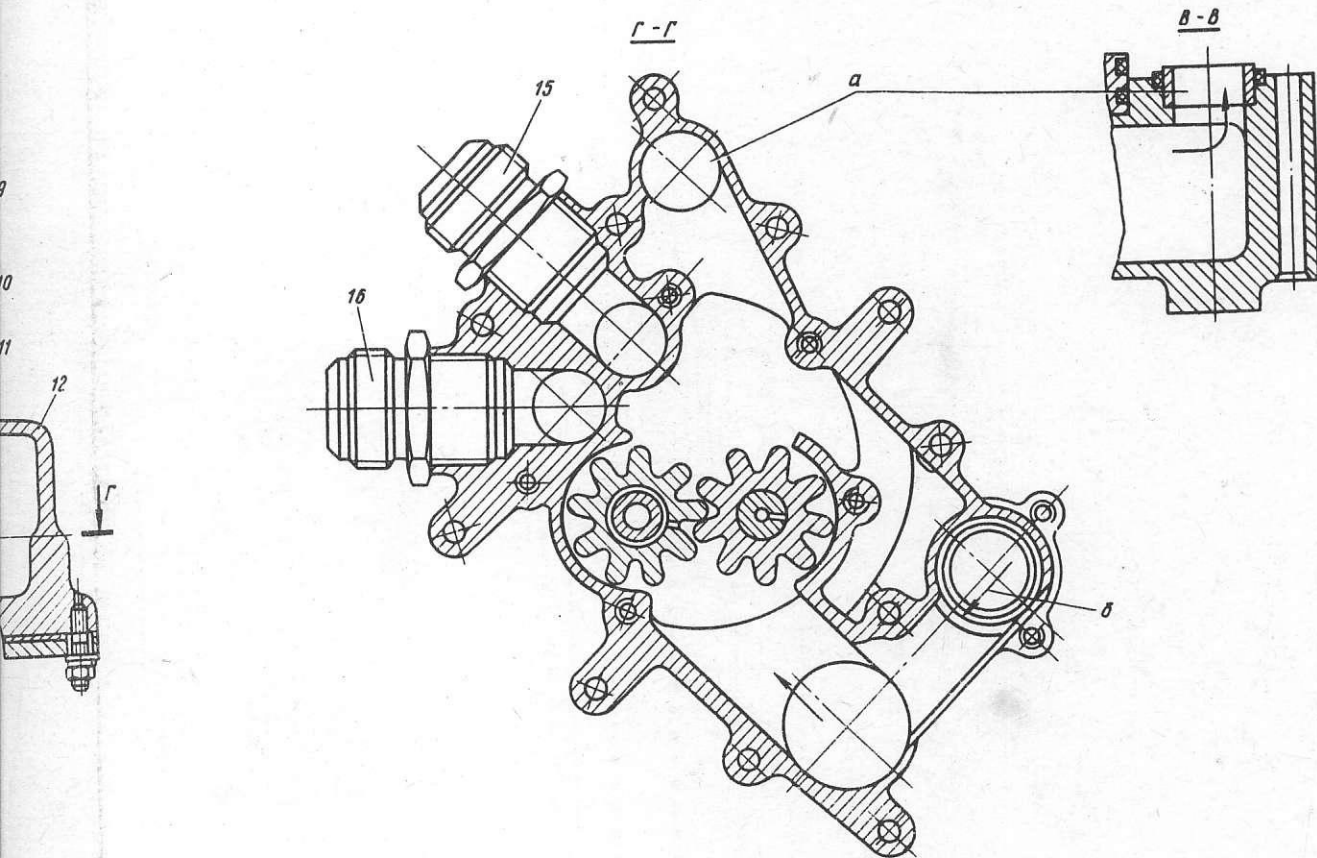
Schmierstoffaggregat des Hauptgetriebes
